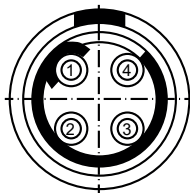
Löt-schema des Steckverbinders am Kabel
